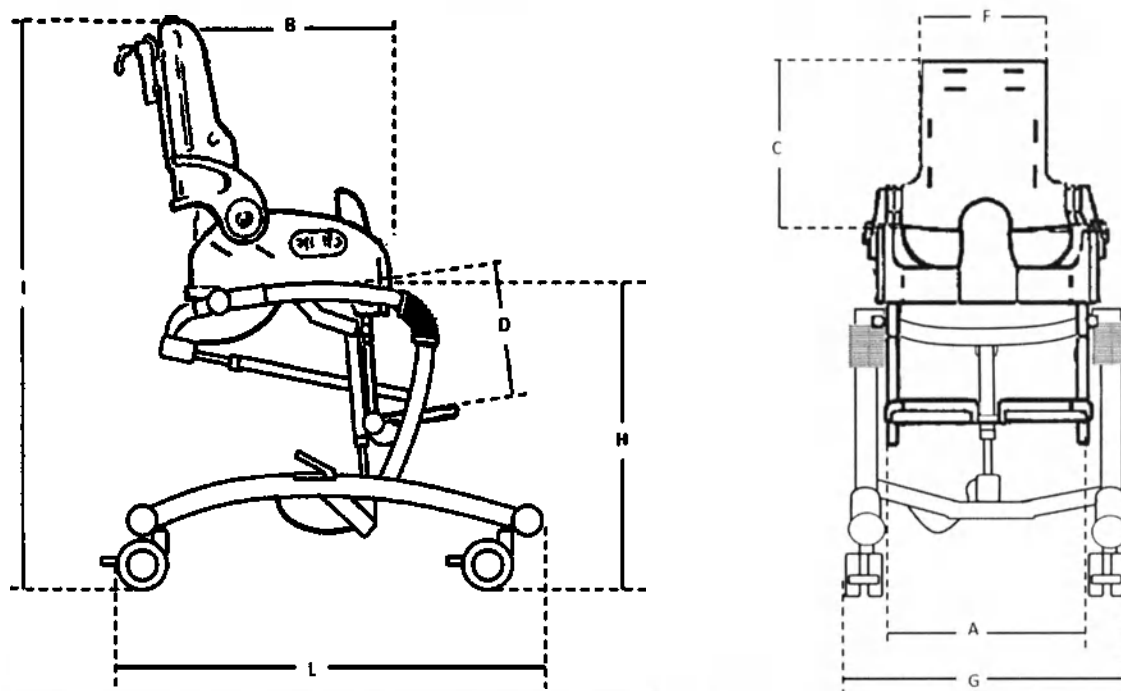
Обозначение основных размеров кресла-стула с санитарным оснащением Фламинго РУ (FLAMINGO RU)
